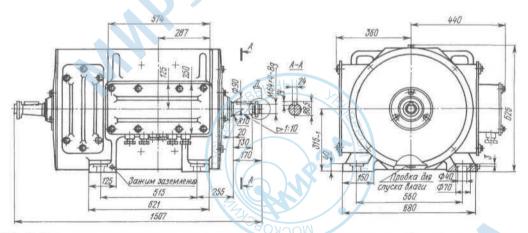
Габаритные, установочно-присоединительные размеры двигателя без тормоза тип "ДПМ 62"
